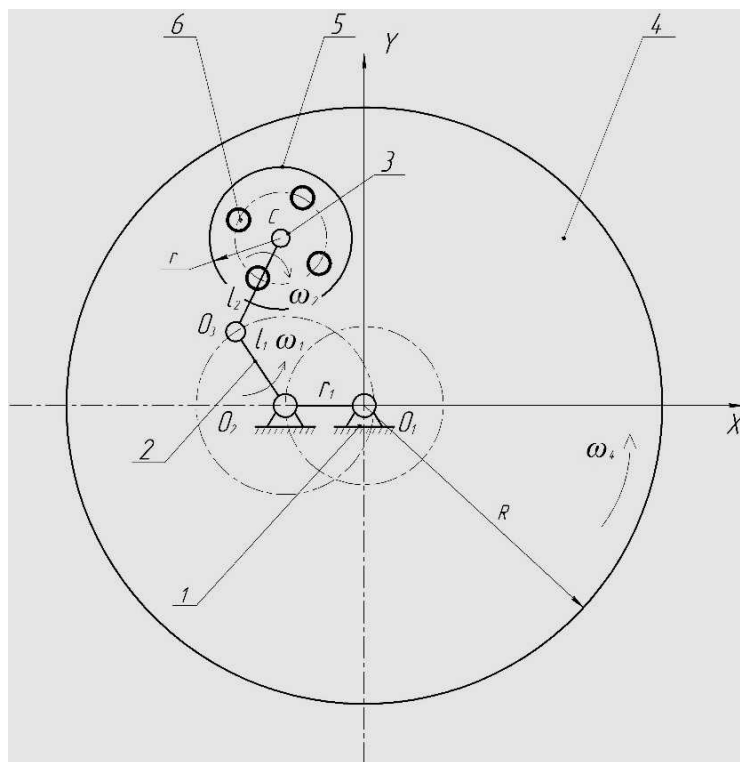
Кинематическая схема комплекса в процессе обработки (вид сверху)
